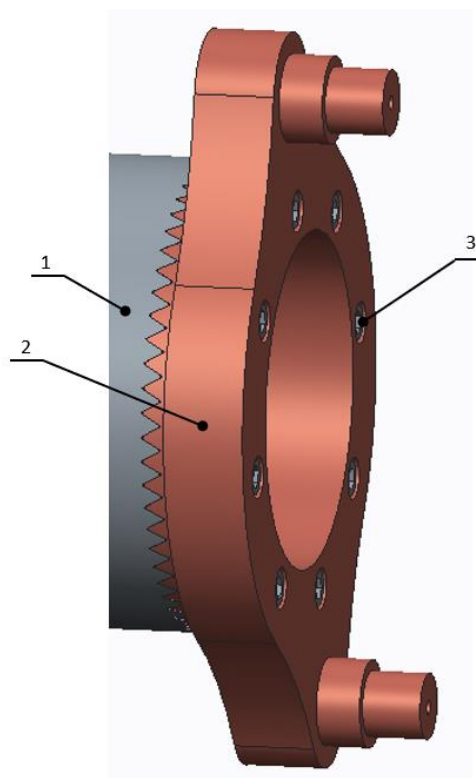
Pružná spojka; 1 - rotor, 2 – unašeč, 3 – ojničky, 4 – paleta, 5 – unašeč nápravy
